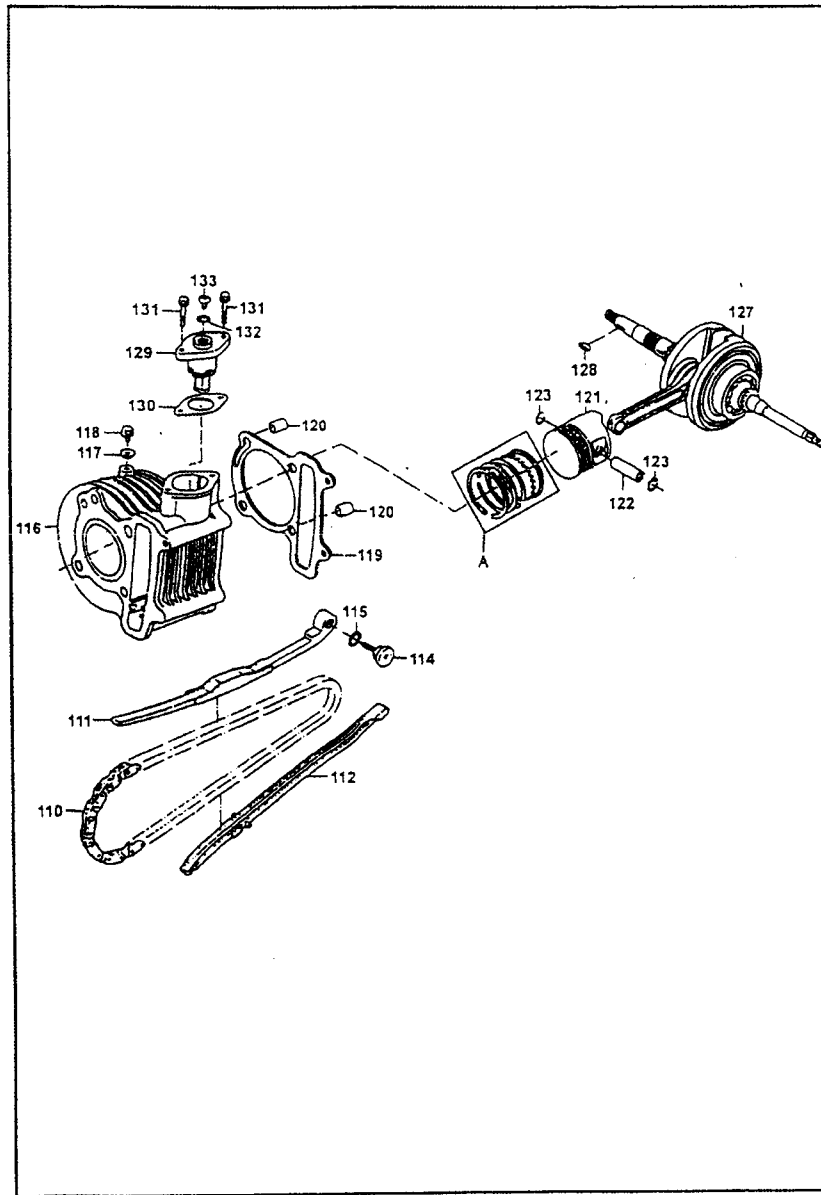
汽缸.活塞.曲轴 CYLINDER.C RANKCASE.P PISTON
